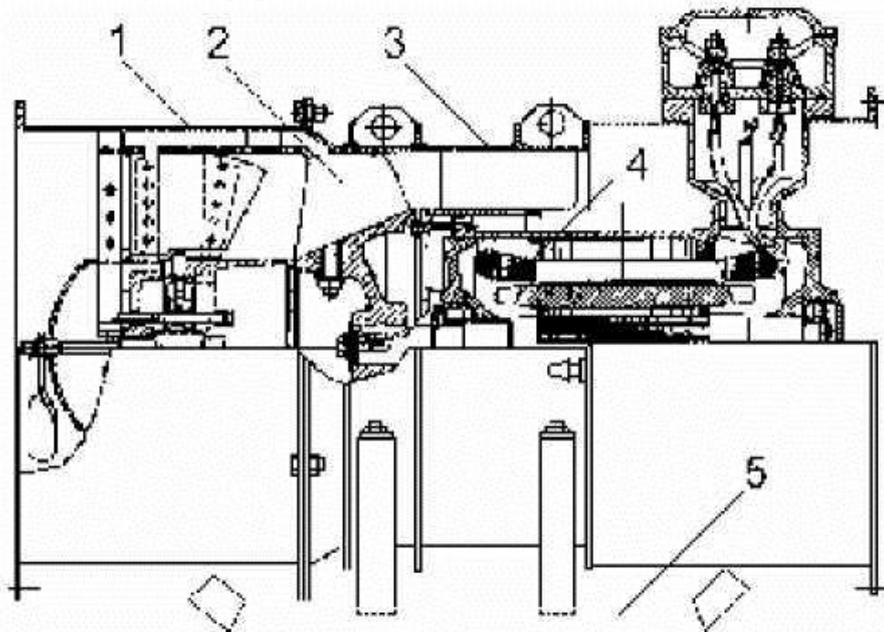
Вентилятор ВМ-5М: 1 - корпус; 2 - рабочее колесо; 3 - спрямляющий аппарат; 4 - электродвигатель; 5 - салазки
